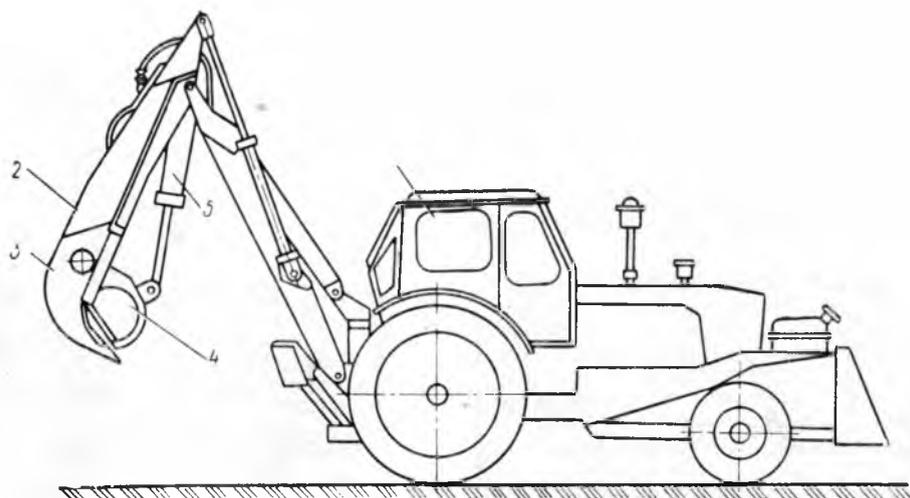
Механизм обрезки вершин на базе экскаватора ЭО-26-21:
